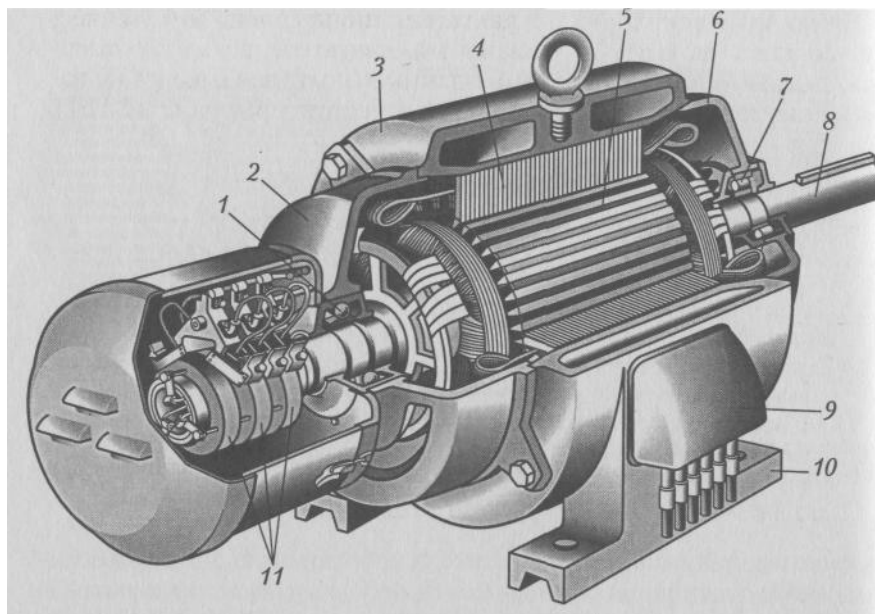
Общий вид конструкции асинхронной машины с фазным ротором: 1 – подшипник с не приводным концом, 2 – подшипниковый щит с не приводным концом, 3 – корпус, 4 – сердечник статора, 5 – сердечник ротора, 6 – подшипниковый щит с приводным концом, 7 – подшипник с приводным концом, 8 – вал, 9 – коробка выводов, 10 – опорная лапа, 11 – щеточно-контактный узел
